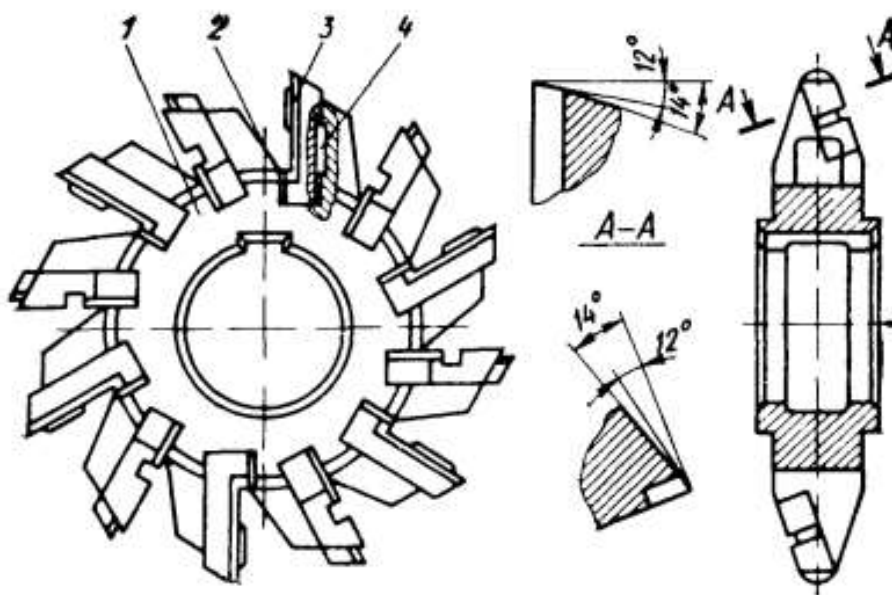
Диска фреза з шаховим розміщенням зубів [5]
